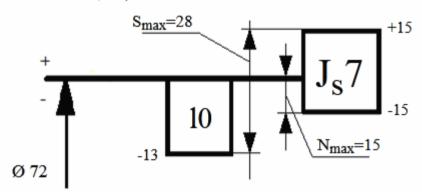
Поля допусков и показатели точности посадки для сопряжения наружного кольца подшипник с отверстием корпуса
